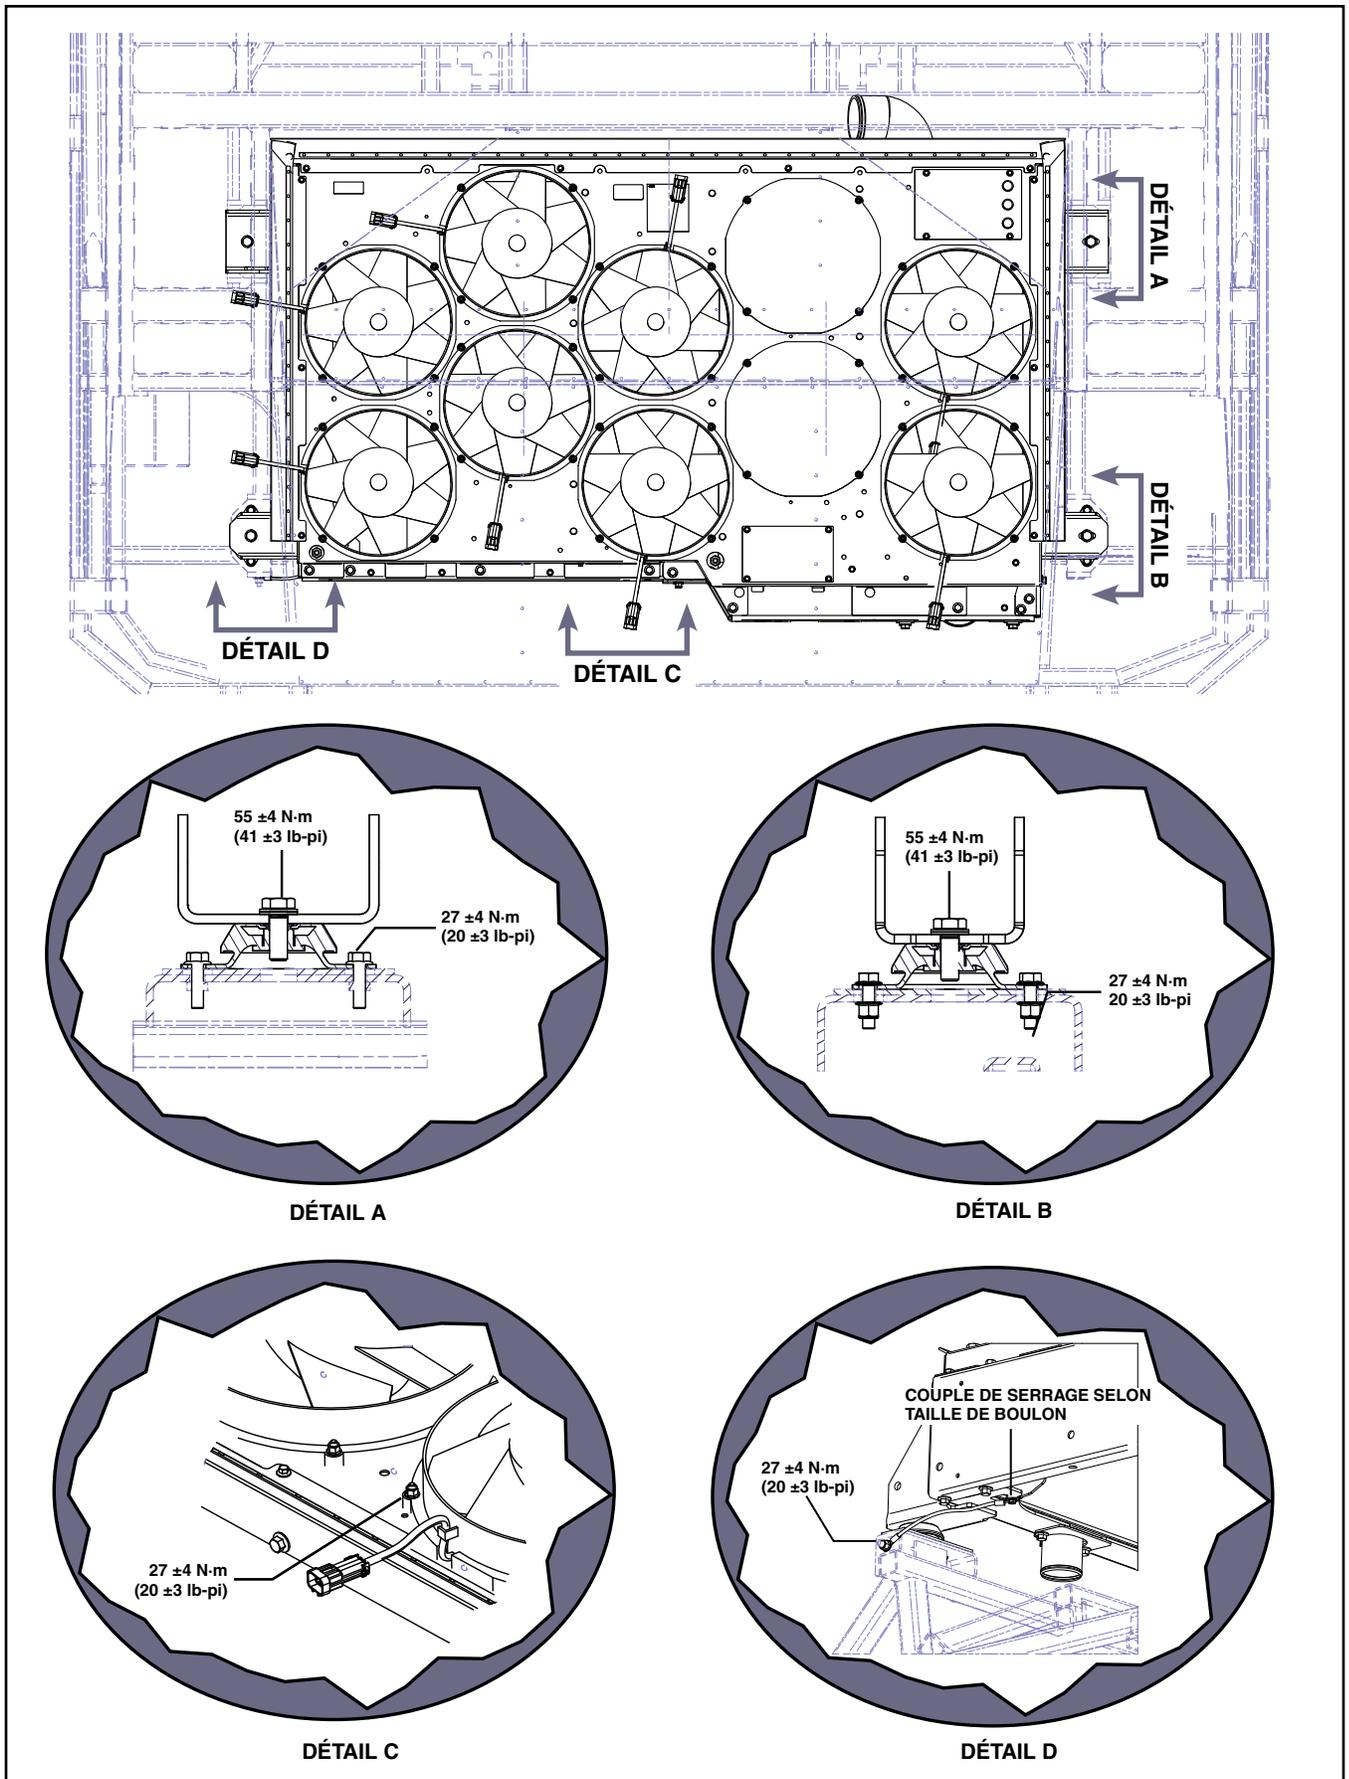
Installation de l'ensemble de refroidissement et couples de serrage
